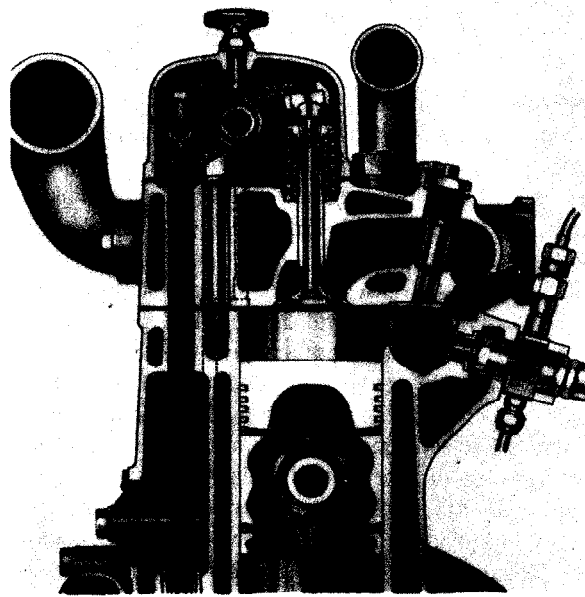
Cámara de turbulencia (indicada por una flecha) e inyector en el motor Diesel Hercules (Hercules Motors Corporation).
